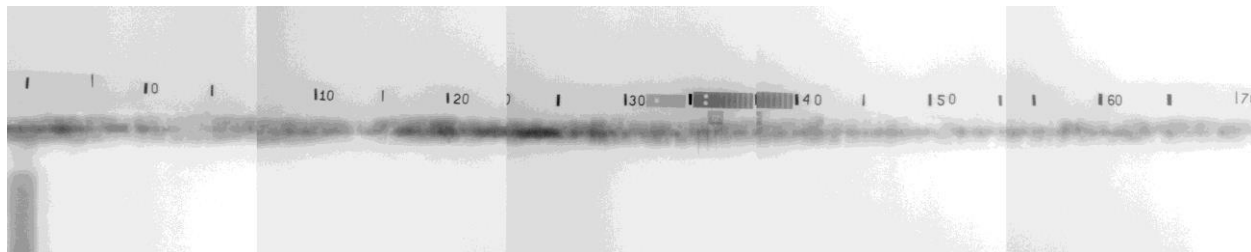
Часть исходных кадров сварного шва
